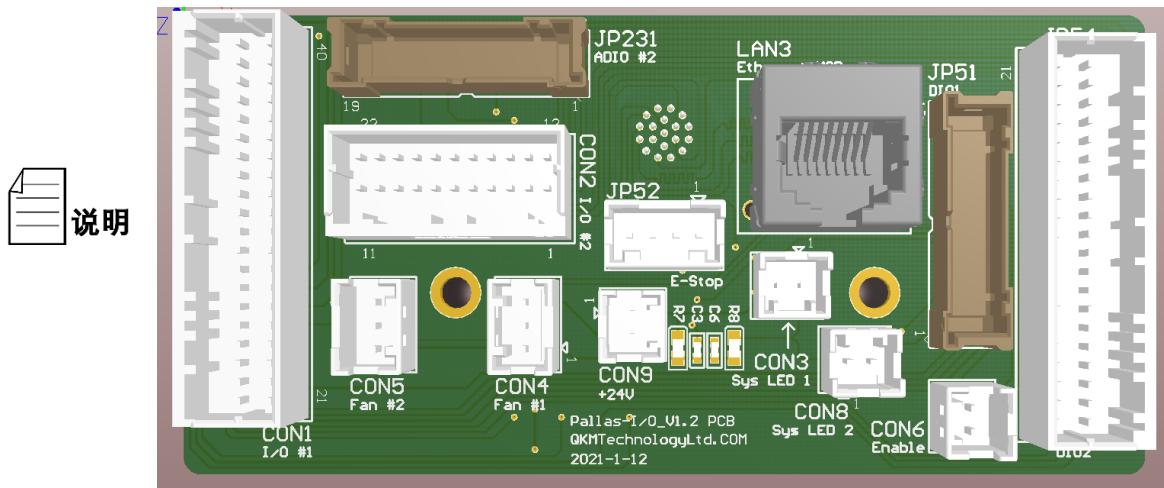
I/O 自由分配 PCBA 螺母拆卸示意图
